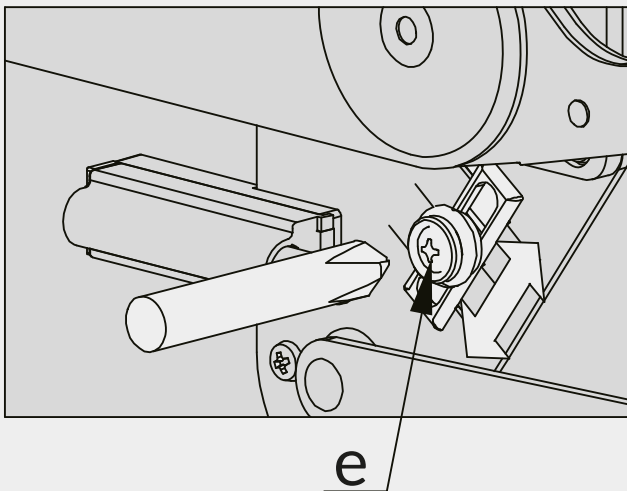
Dévisser les vis "e" sur les deux côtés, régler la hauteur de la porte. Resserrer.
